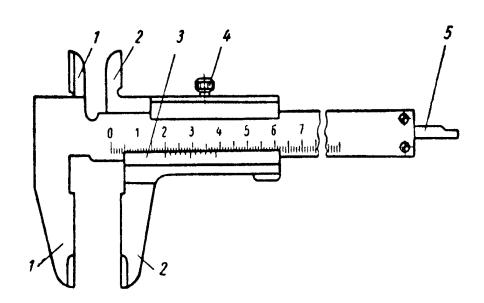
Штангенциркуль ШЦ-І:
